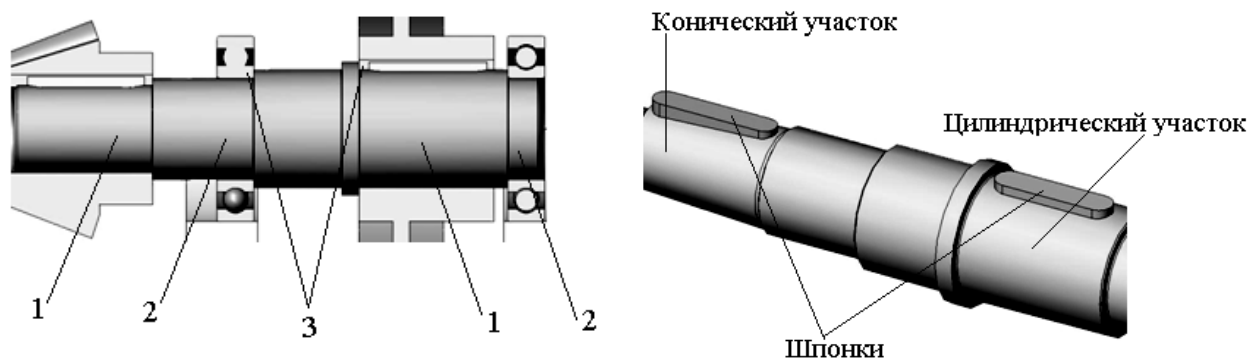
Вал с конструктивными элементами: 1 — посадочная поверхность (посадочный участок), 2 — цапфа, 3 — переходная поверхность (переходный участок)
